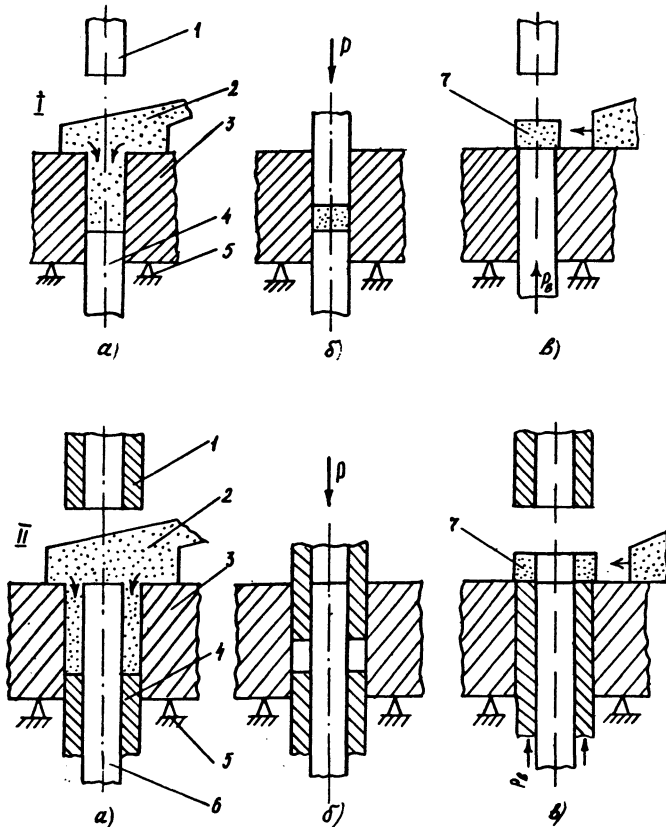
Схема одностороннего прессования цельных (I) и полых (II) изделий: а - загрузка порошковой шихты; б - прессование; в - выпрессовывание брикетов; 1 - верхний пуансон; 2 - загрузочный бункер; 3 - матрица; 4 - нижний пуансон; 5 - упор; 6 - игла-стержень; 7 - прессовка (брикет); $P_{\text{в}}$ - сила выталкивания
